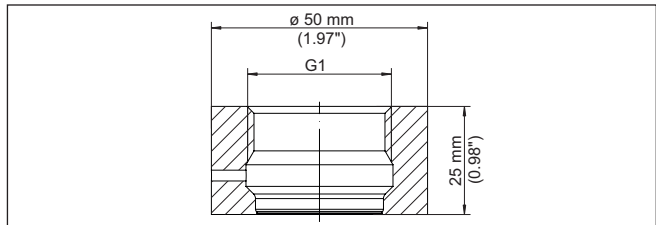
Dimensiones racor para soldar G1 (ISO 228-1) - Junta tórica
